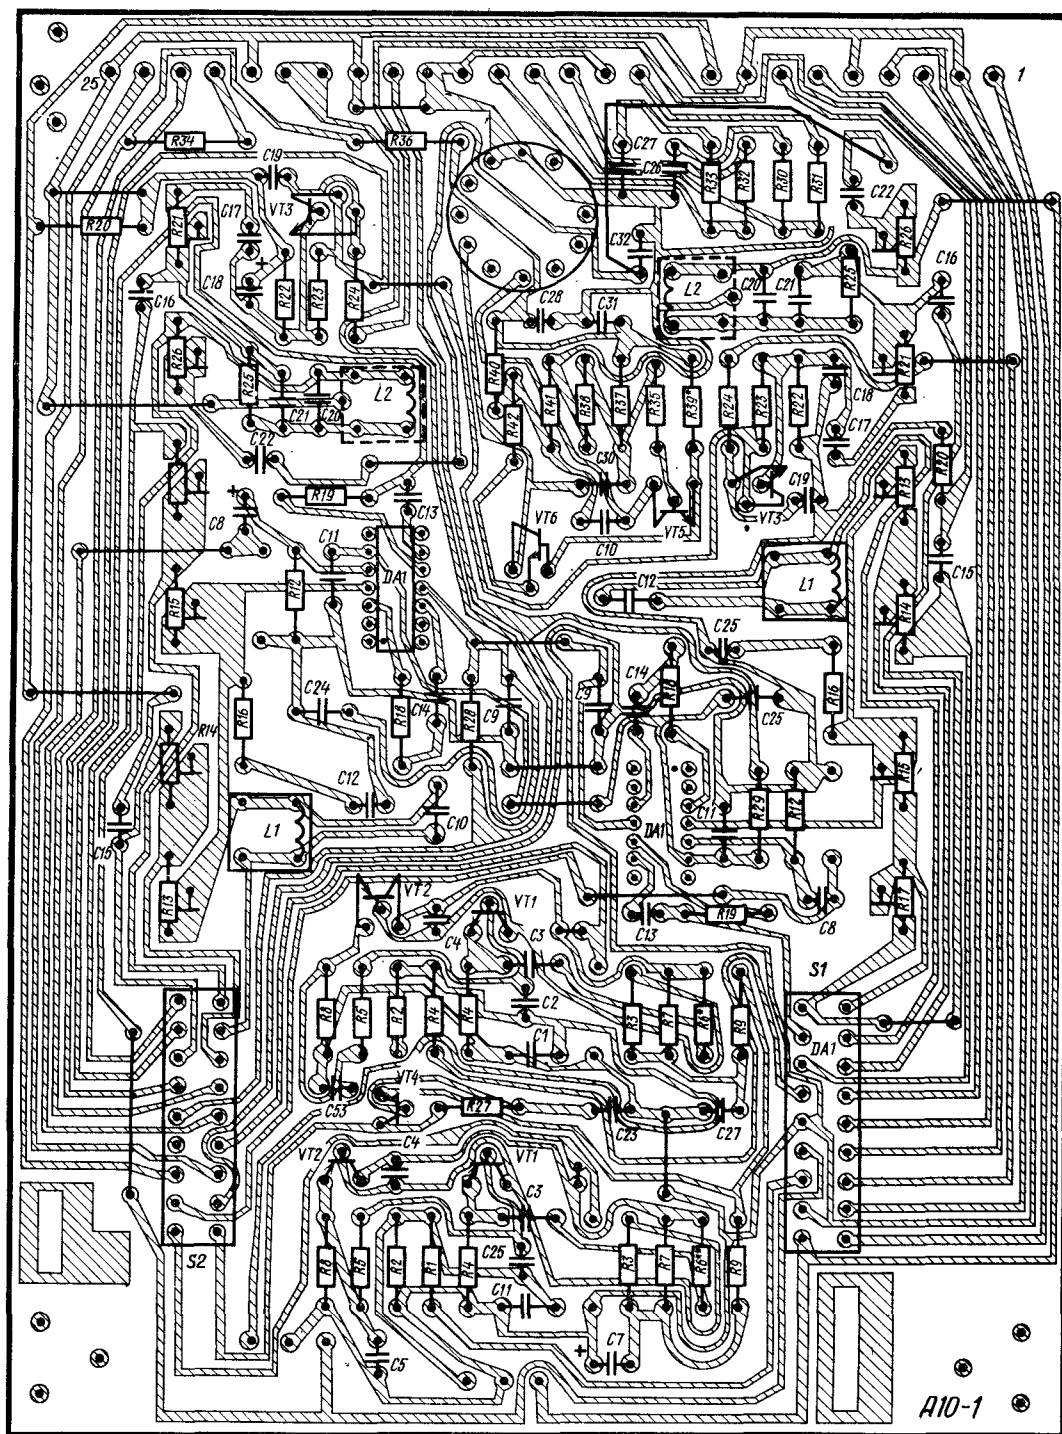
Электромонтажная схема печатной платы блока универсального УЗВ (A10-1)
